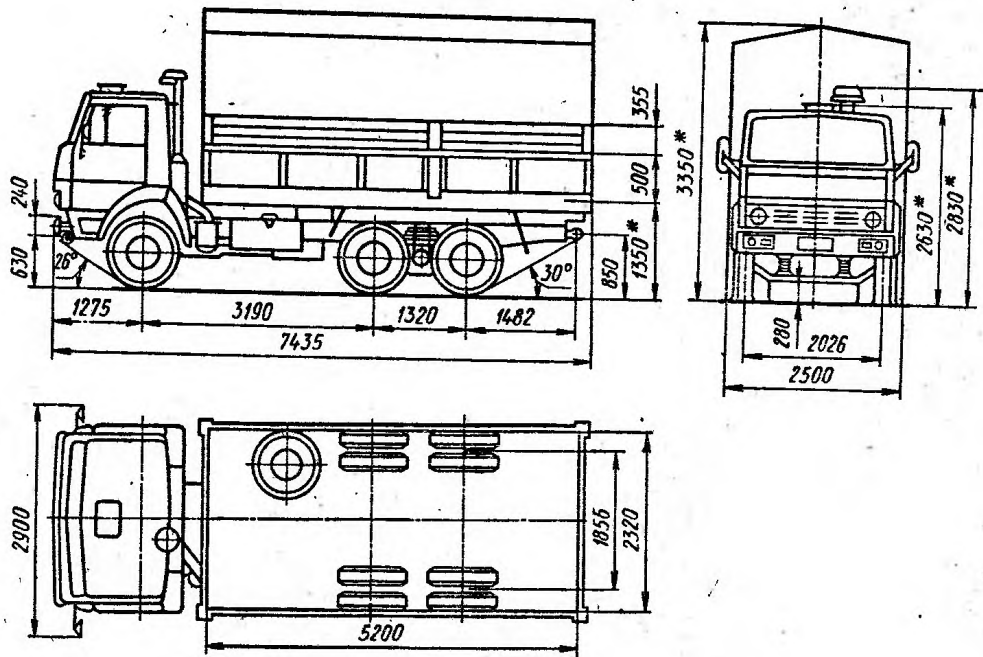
Габаритные размеры автомобиля КамАЗ-5320 (здесь и далее звездочкой отмечены размеры для снаряженного автомобиля).
